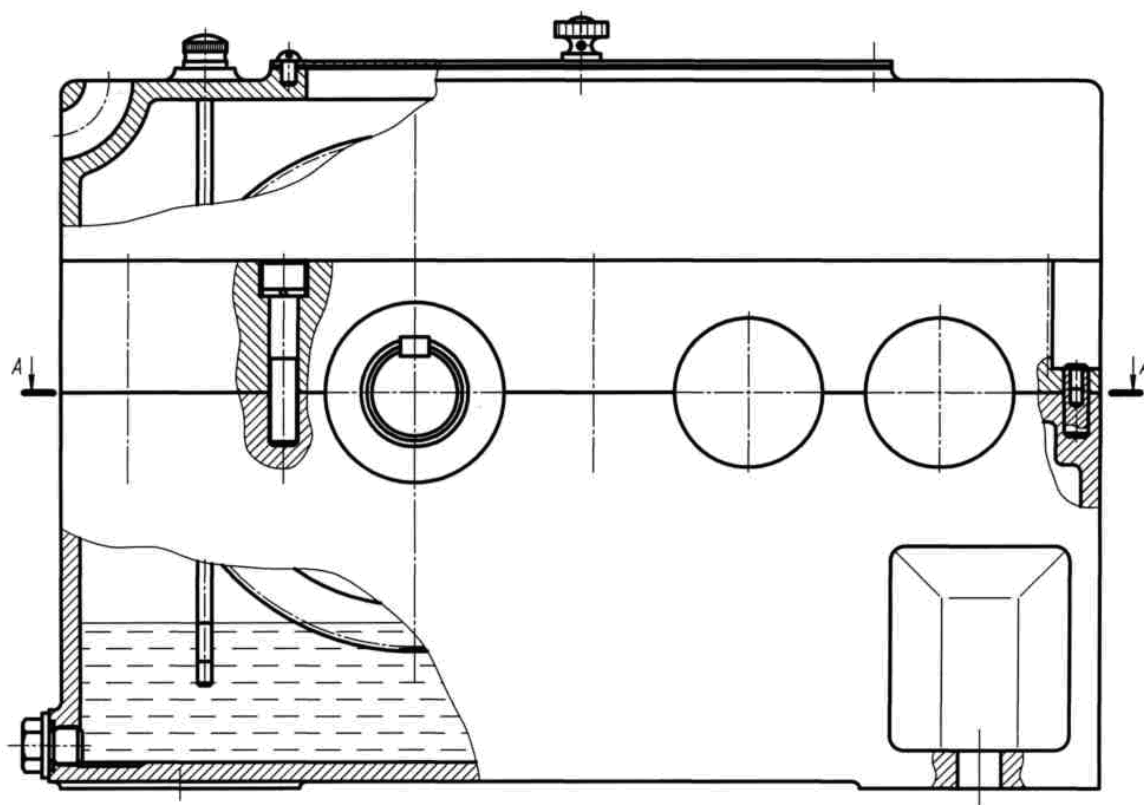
Редуктор двухступенчатый цилиндрический соосный вертикальный
